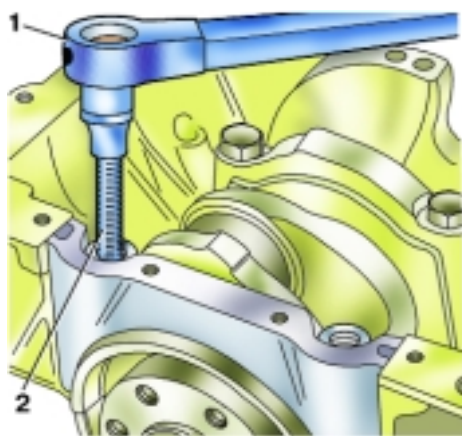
Затяжка болтов крепления крышки 1-го коренного подшипника коленчатого вала двигателя F3R 272: 1 – динамометрический ключ; 2 – наконечник
